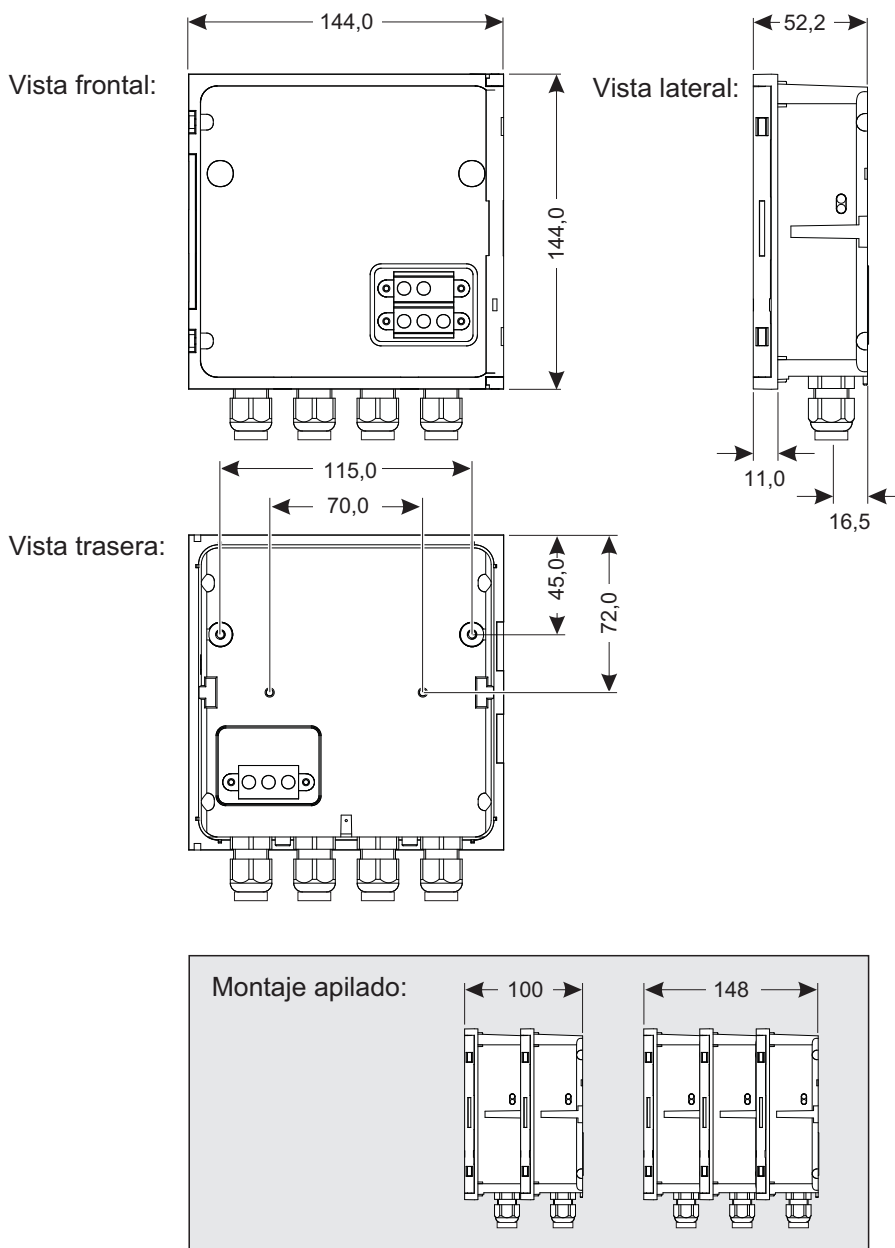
Dibujo acotado del módulo MIQ (dimensiones en mm)
